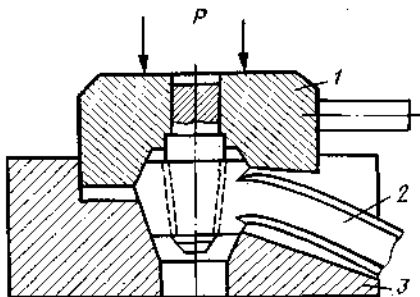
Приспособление для обжатия конусного отверстия рулевой сошки:
